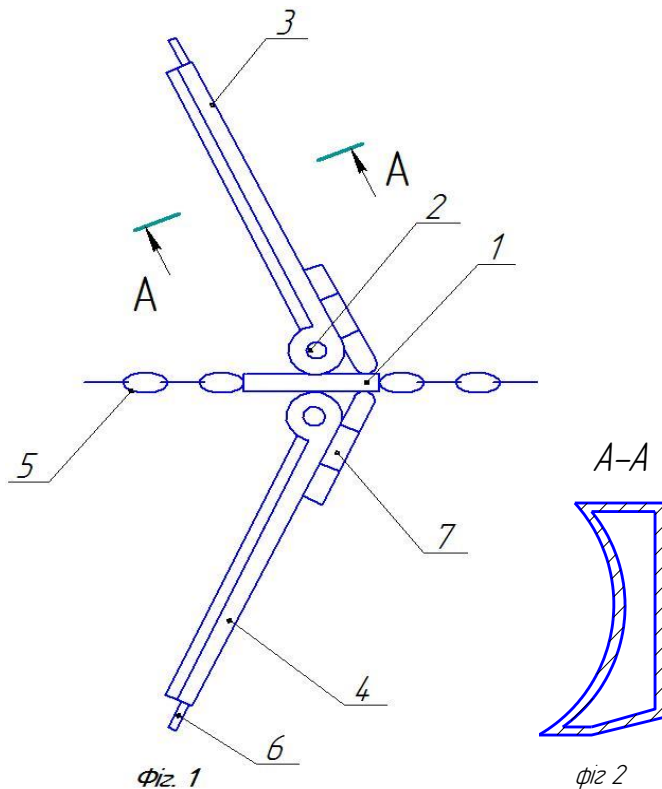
Розроблений скреперний пристрій для прибирання гною
